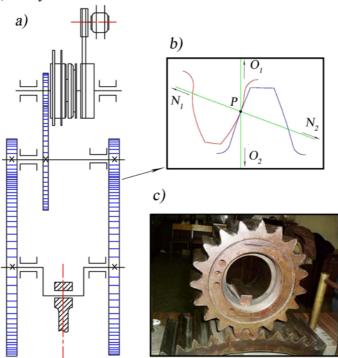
Примеры зубчатых передач с большим передаточным отношением.
